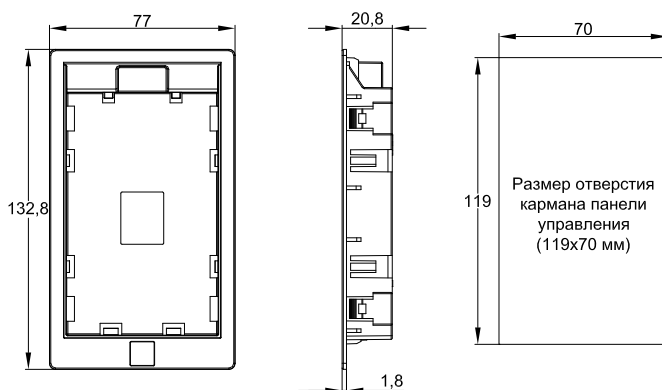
Габаритные размеры держателя внешней цифровой двухстрочной панели управления (единица измерения – мм)
